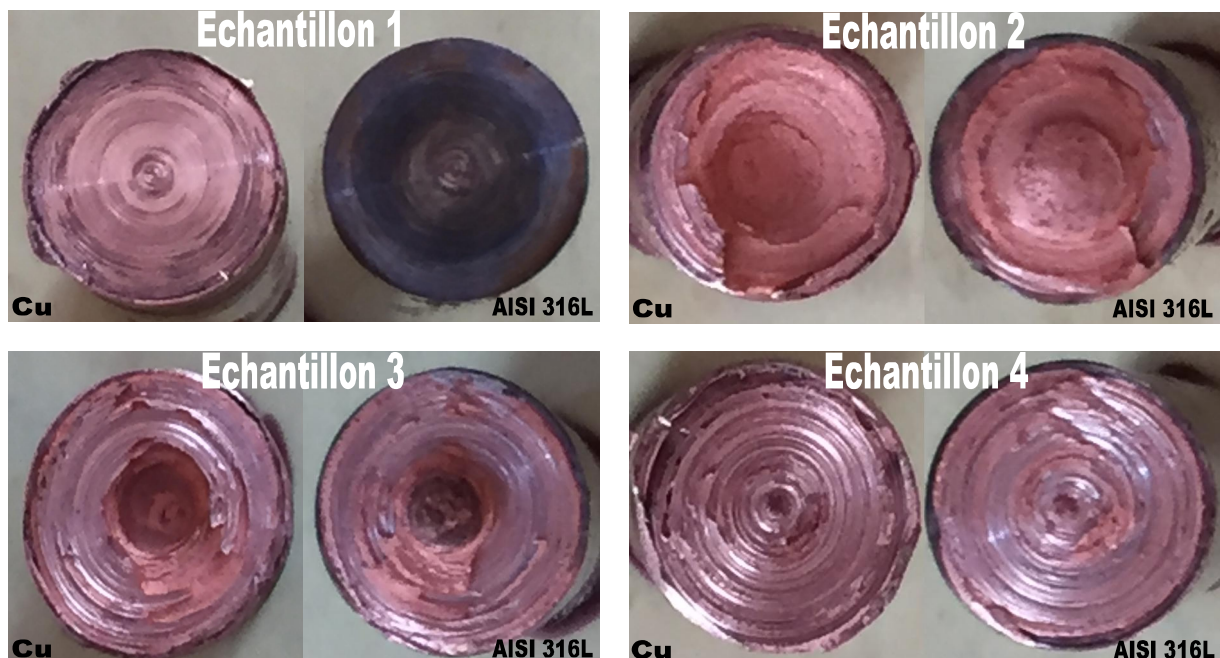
Fractographie des échantillons soudés acier inoxydable AISI 316L/cuivre après les tests de traction.
